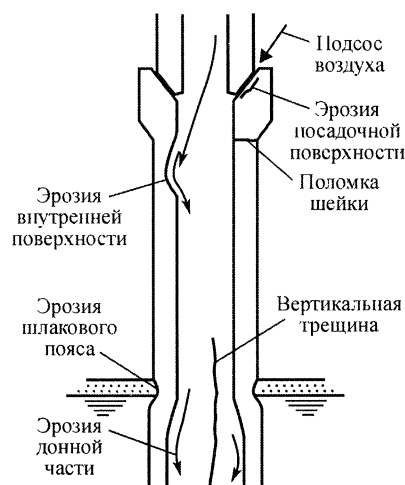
Схема футеровки сталеразливочного тракта:
